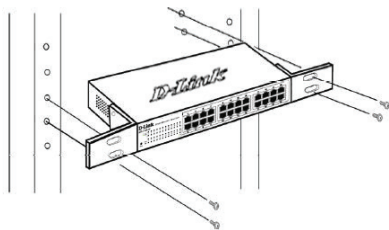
Montage der DFL-260E / 860E im Rack oder Gehäuse
